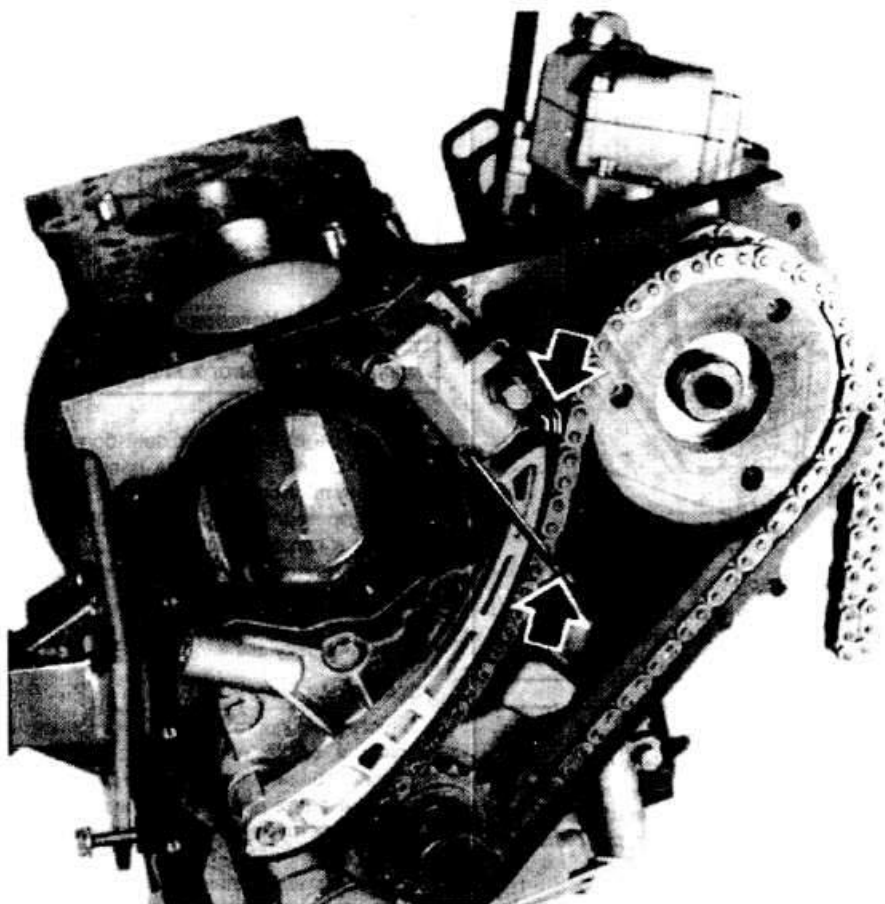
Блокировка плунжера натяжителя цепи с помощью фиксатора
